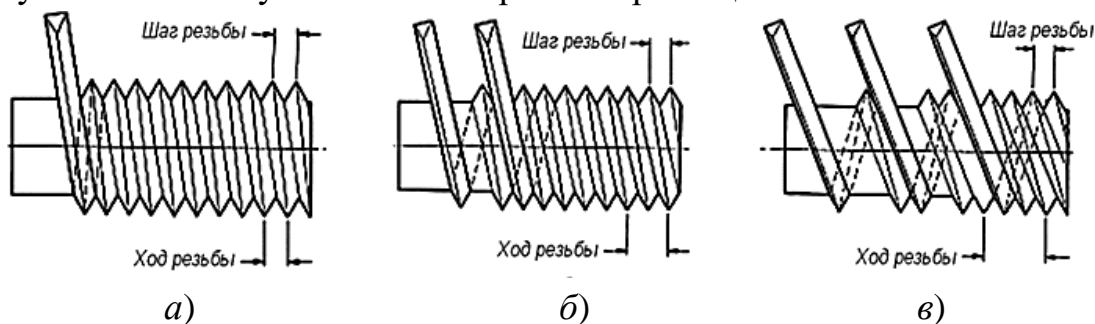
Ход резьбы: а - однозаходная резьба; б – двухзаходная резьба; в – трехзаходная резьба
